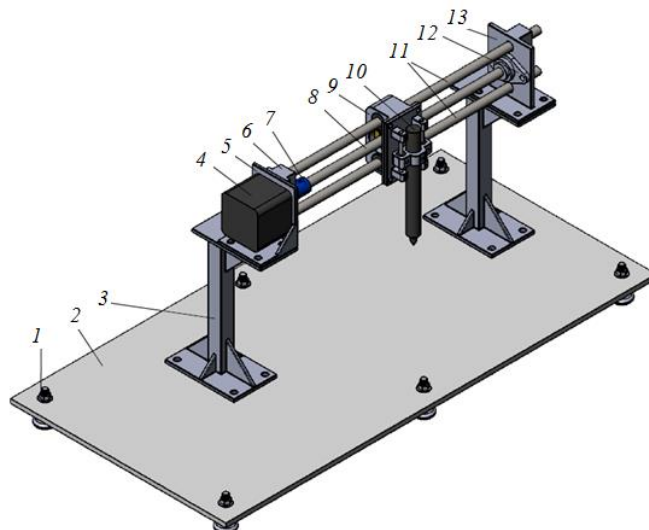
Узел продольного перемещения рабочего органа макета автоматической установки для обработки отверстий: 1 – регулируемая опора; 2 – основание; 3 – опоры; 4 – привод; 5 – держатель для привода; 6 – узел подшипниковый; 7 – муфта; 8 – шпилька резьбовая; 9 – узел рабочего органа; 10 – маркер; 11 – направляющие цилиндрические; 12 – упор подшипниковый; 13 – крепление для подшипникового упора
